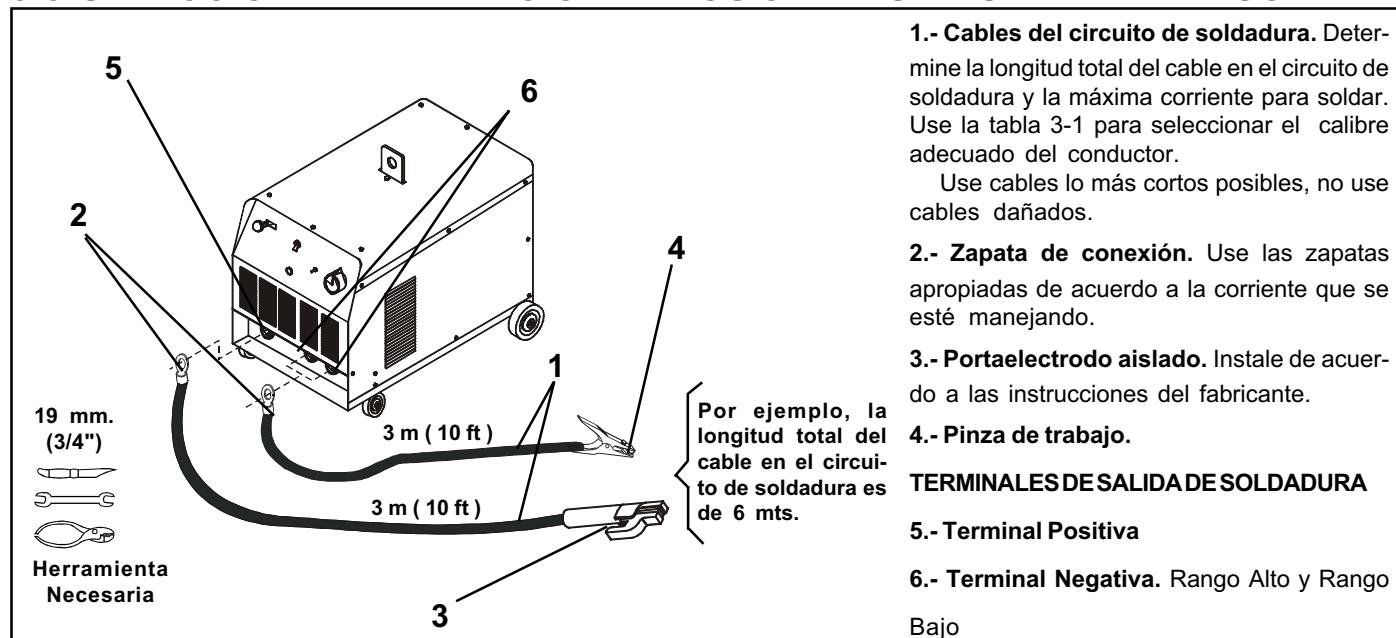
SELECCION DE LOS CABLES PARA SOLDAR
